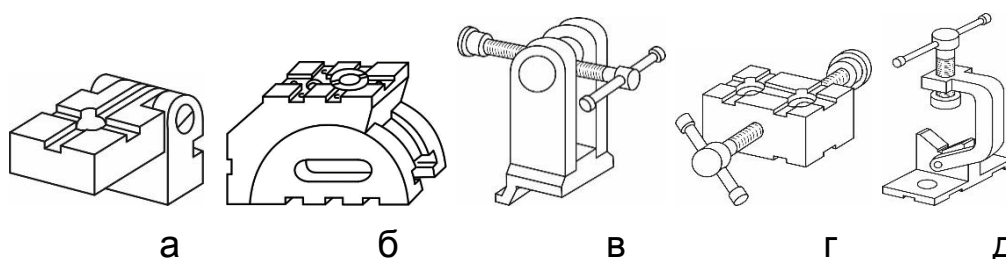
Примеры сборочных единиц: а – головка поворотная; б – опора поворотная; в, г, д – зажимы винтовые
